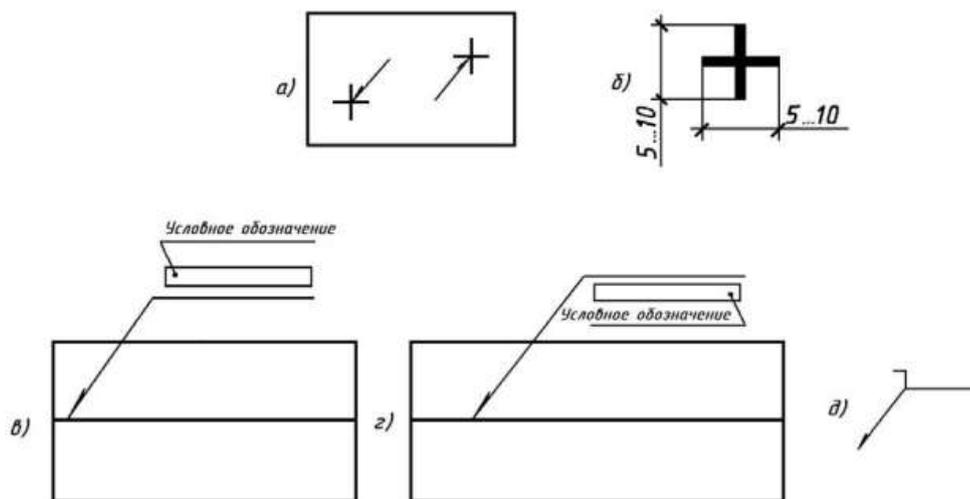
Графическое обозначение сварных швов:
